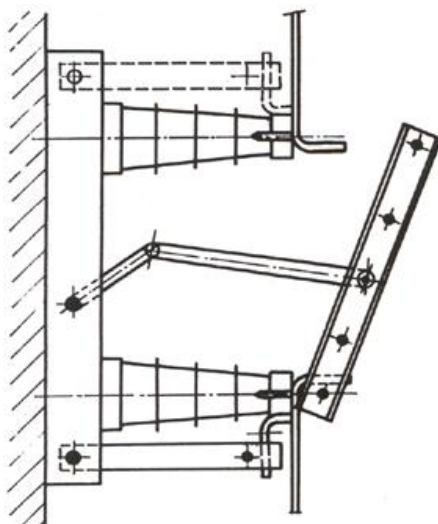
Příklad konstrukce otočných odpojovačů tří dvou izolátorových
